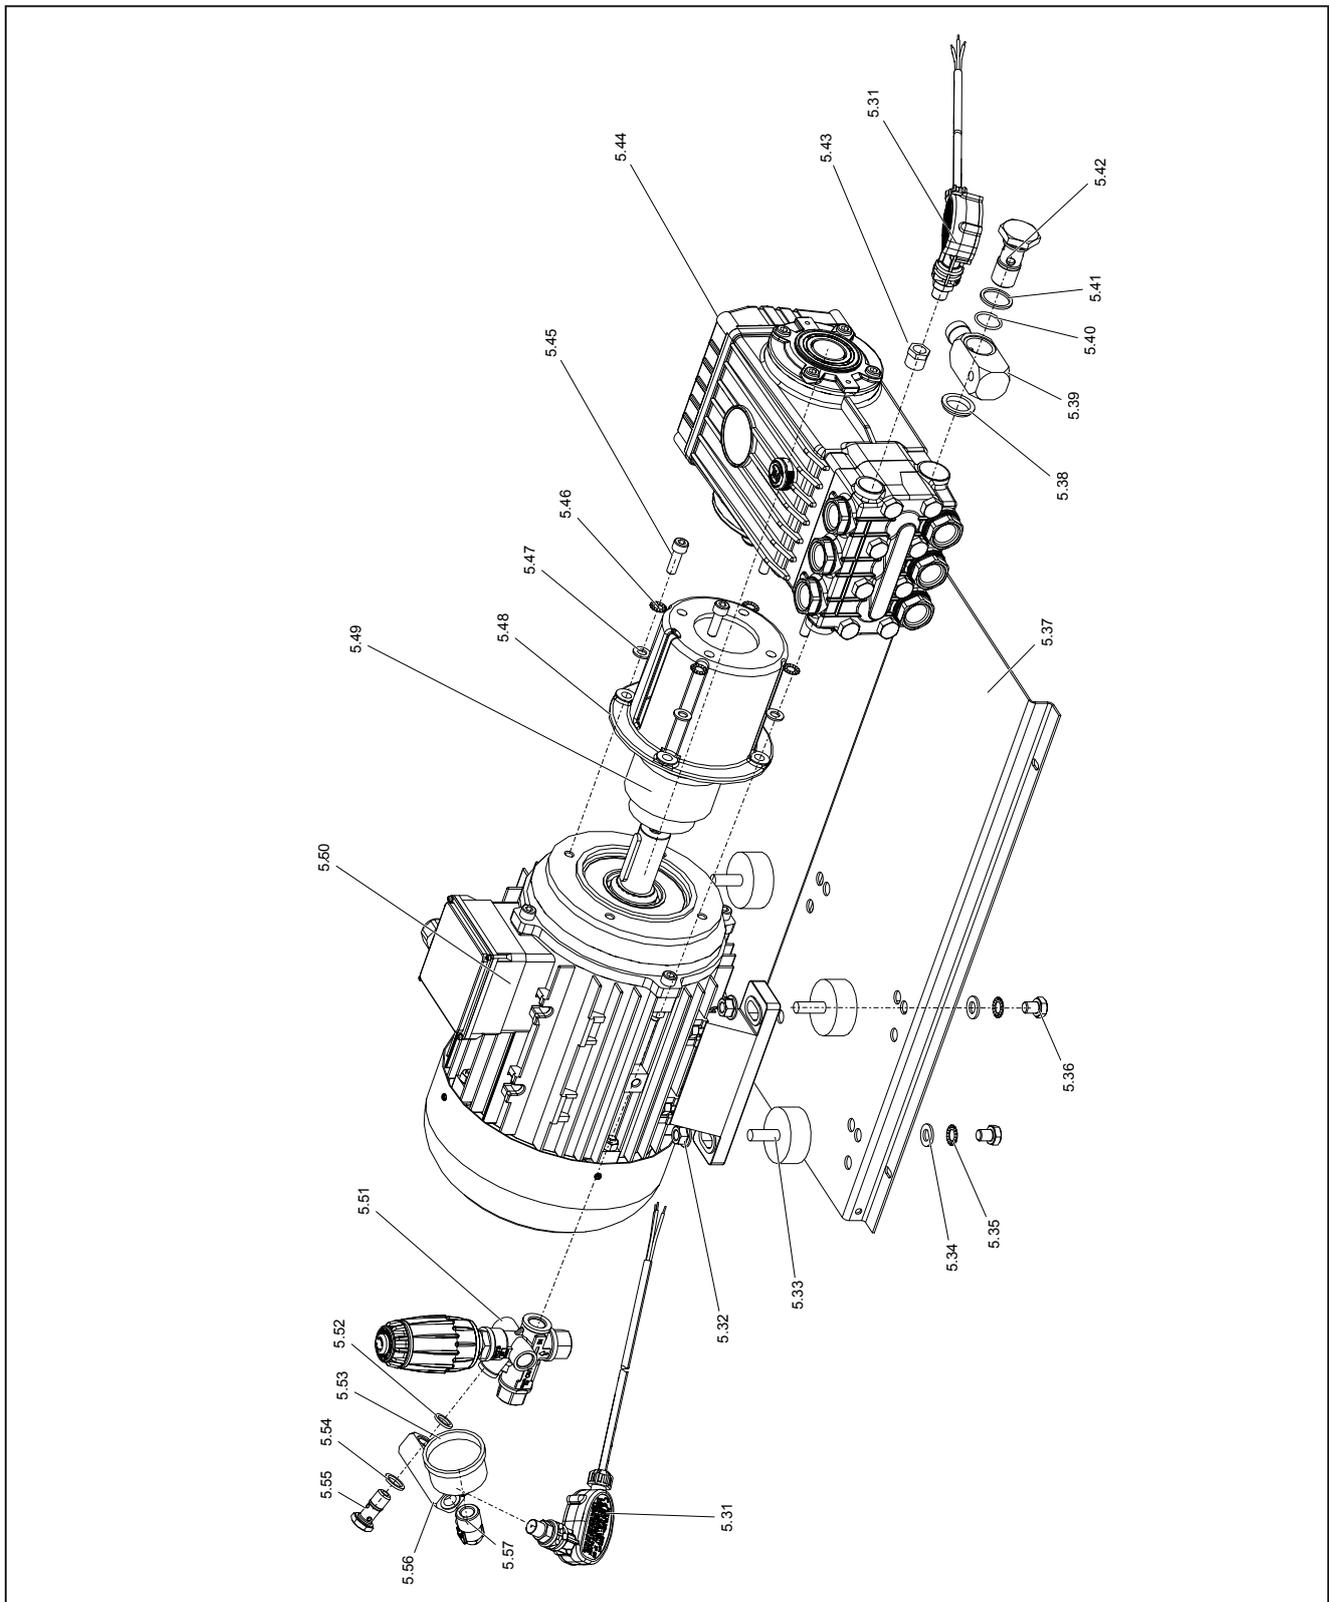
6 Antriebseinheit Motor und Pumpe, Explosionszeichnung
